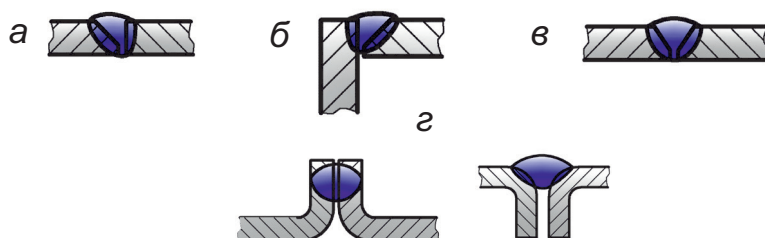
Односторонние сварные швы с разными видами подготовки кромок:
